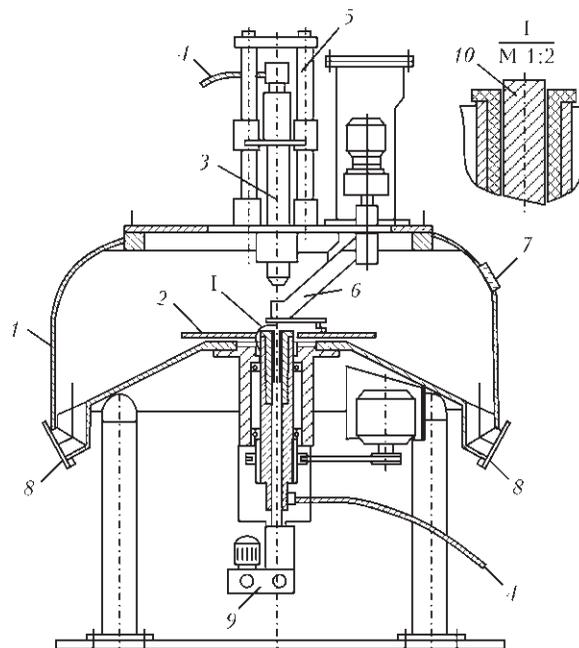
Схема установки для распыления слитков: 1 — корпус камеры; 2 — шпиндельный узел; 3 — плазмотрон; 4 — токоподвод; 5 — механизм регулировки плазмотрона; 6 — механизм загрузки стержня; 7 — смотровое окно; 8 — сборники готовой продукции; 9 — механизм подачи стержня; 10 — распыляемый стержень
